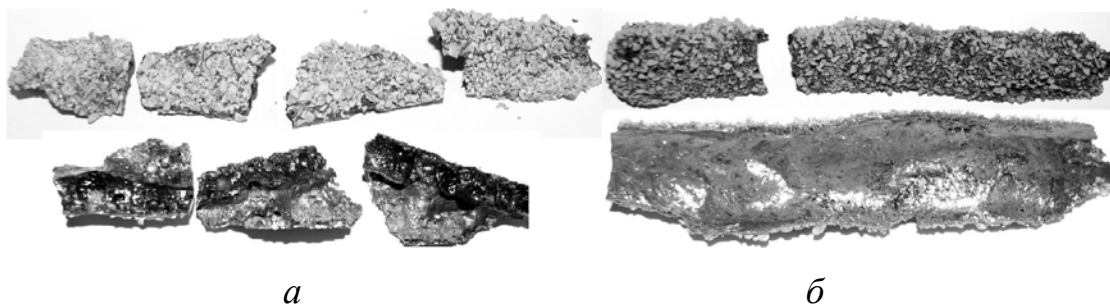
Внешняя и внутренняя поверхность сварочной корки после сварки под слоем флюса (x2): *а* – шлак габбро-диабазы; *б* – шлак горнблендита
